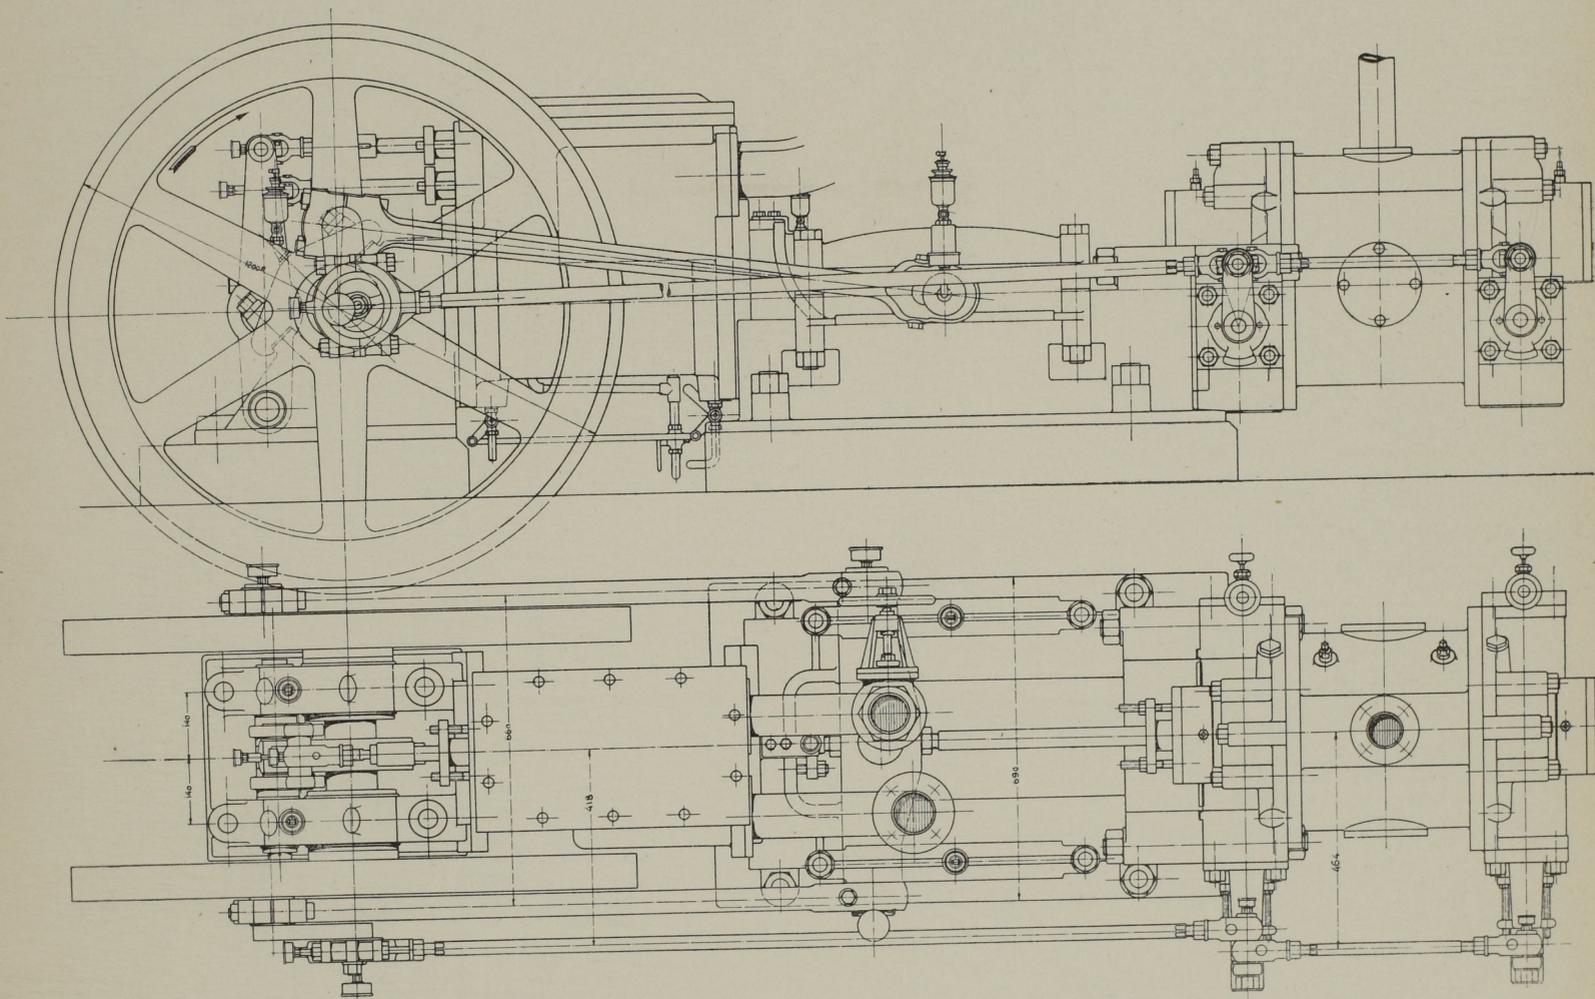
Seitenansicht und Grundriss. Massst. 1:15.
